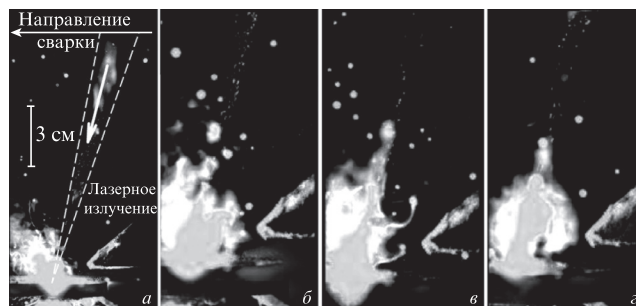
Кадры скоростной видеосъемки сварочного факела в случае падения лазерного излучения на поверхность металла под углом 15° .
